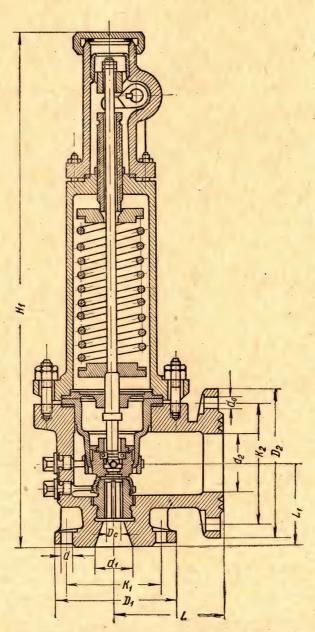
Клапан предохранительный пружинный полноподъемный фланцевый ППК2.
